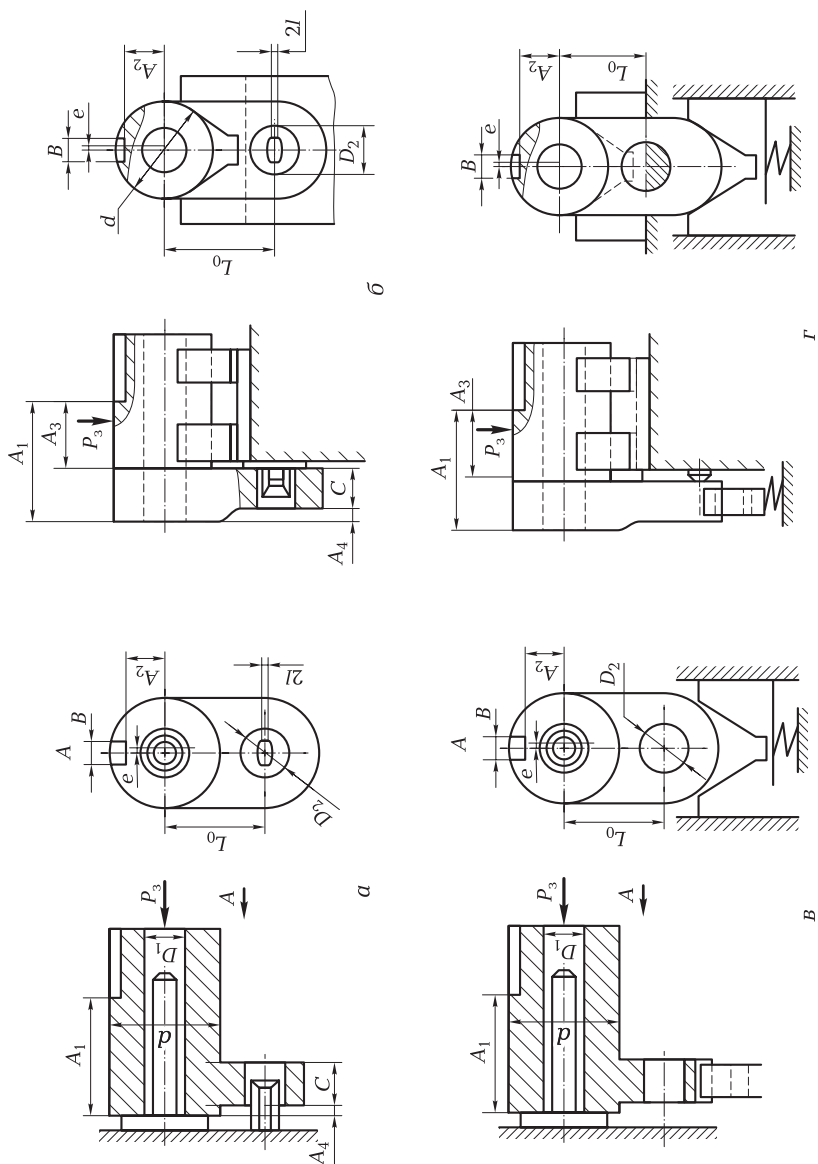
Схема установки заготовки при обработке шпоночного паза (P_3 — сила зажима заготовки)
